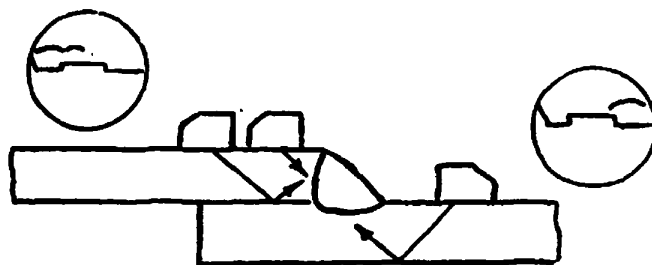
Схемы контроля нахлесточных сварных соединений;
